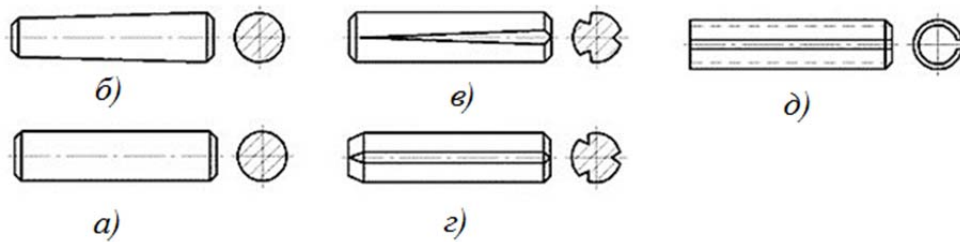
Види штифтів: циліндричний гладкий (а); конічний (б); просічні (в,г); пружинний (д).
